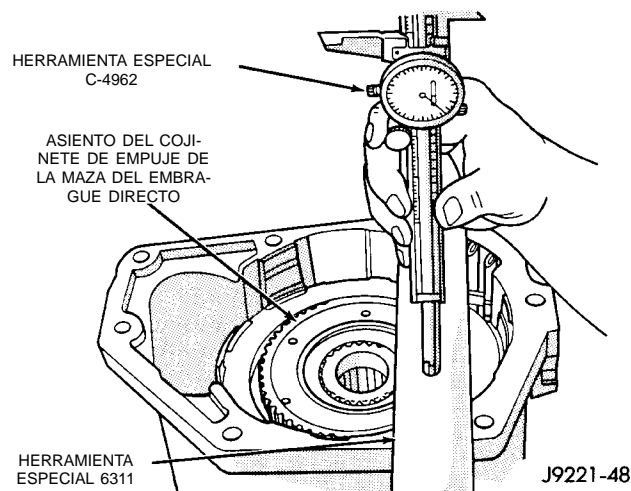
Medición de la placa de empuje del émbolo de sobremarcha
